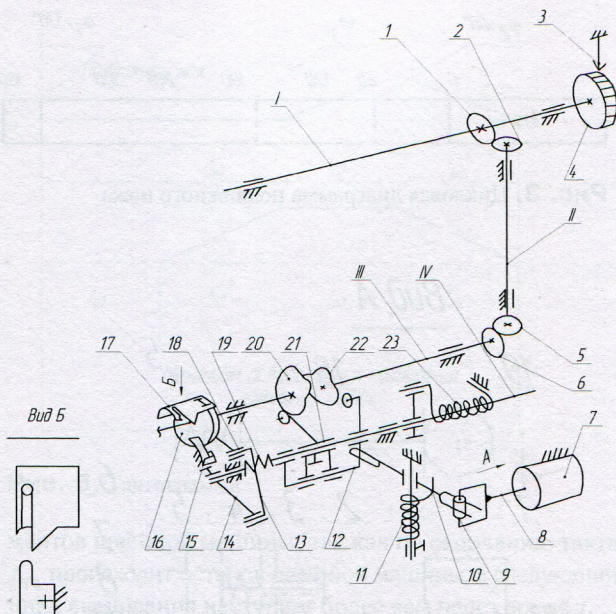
Кинематическая схема механизма автоматической обрезки ниток швейной машины класса GC720 HD фирмы «Typical»
